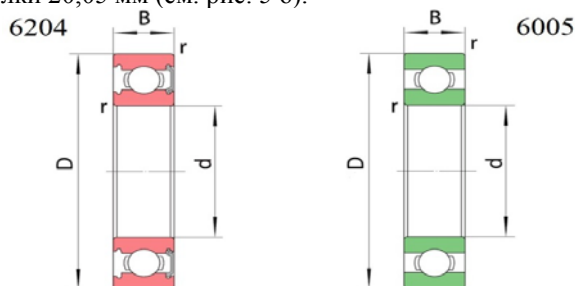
Основные габаритные размеры подшипников марок 6204 и 6005
